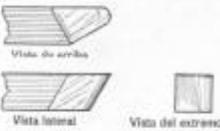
Detalle de la cuchilla para tornear en la izquierda
